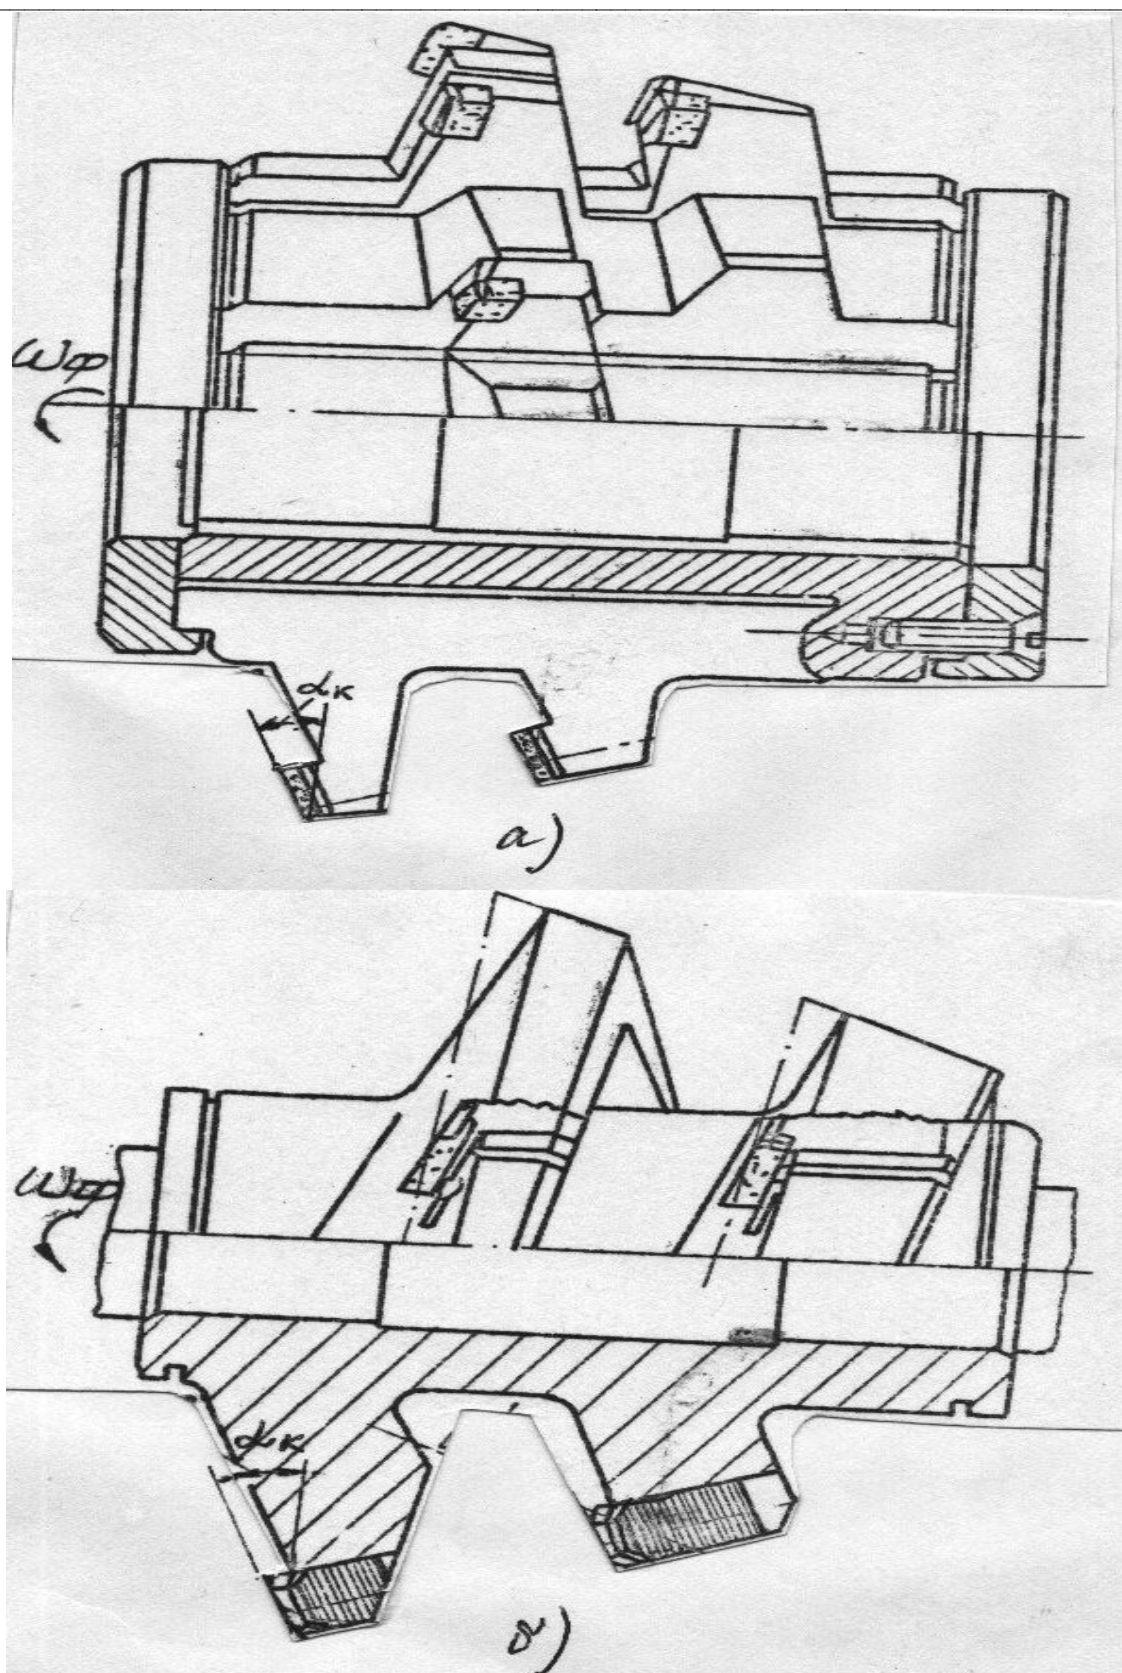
Конструкция специальных твердосплавных фрез. а- правый корпус фрез  $m=10-16$  мм со вставными зубчатыми рейками и напаянными пластинками; б- правый корпус фрез  $m=18-65$  мм со вставными резцами и напаянными пластинками.
